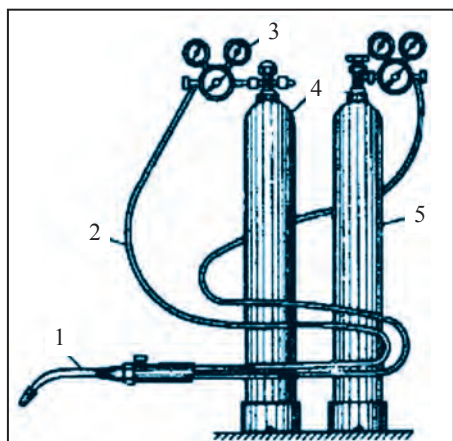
Оборудование для газосварки: 1 – горелка; 2 – шланги; 3 – редуктор; 4 – кислородный баллон; 5 – ацетиленовый баллон.
